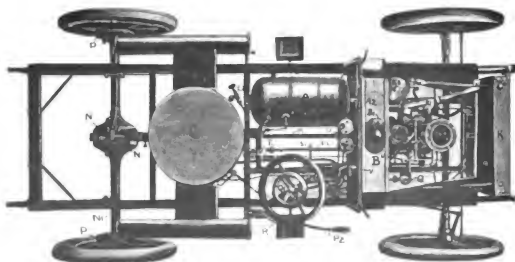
Chassis der White Sewing Mach. Co. im Grundriss.
